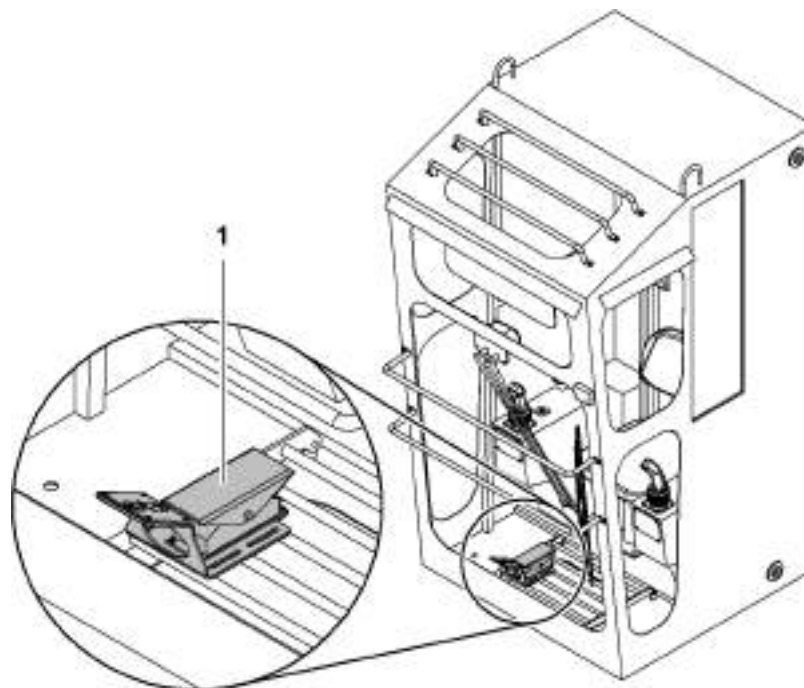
Girar dispositivo oscilante del motor en el sentido de las agujas del reloj
